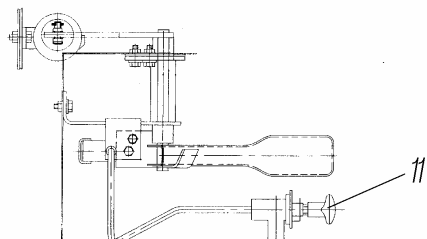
Привод управления подачей топлива и ручного останова двигателя:
